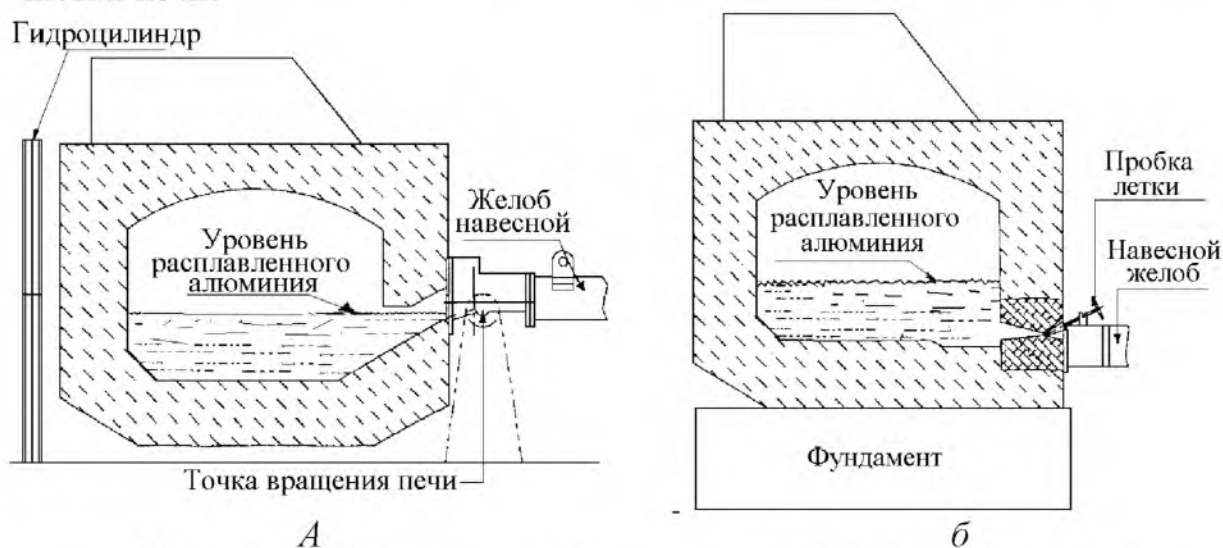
Разрез печи для выплавки алюминиевых столбов:
